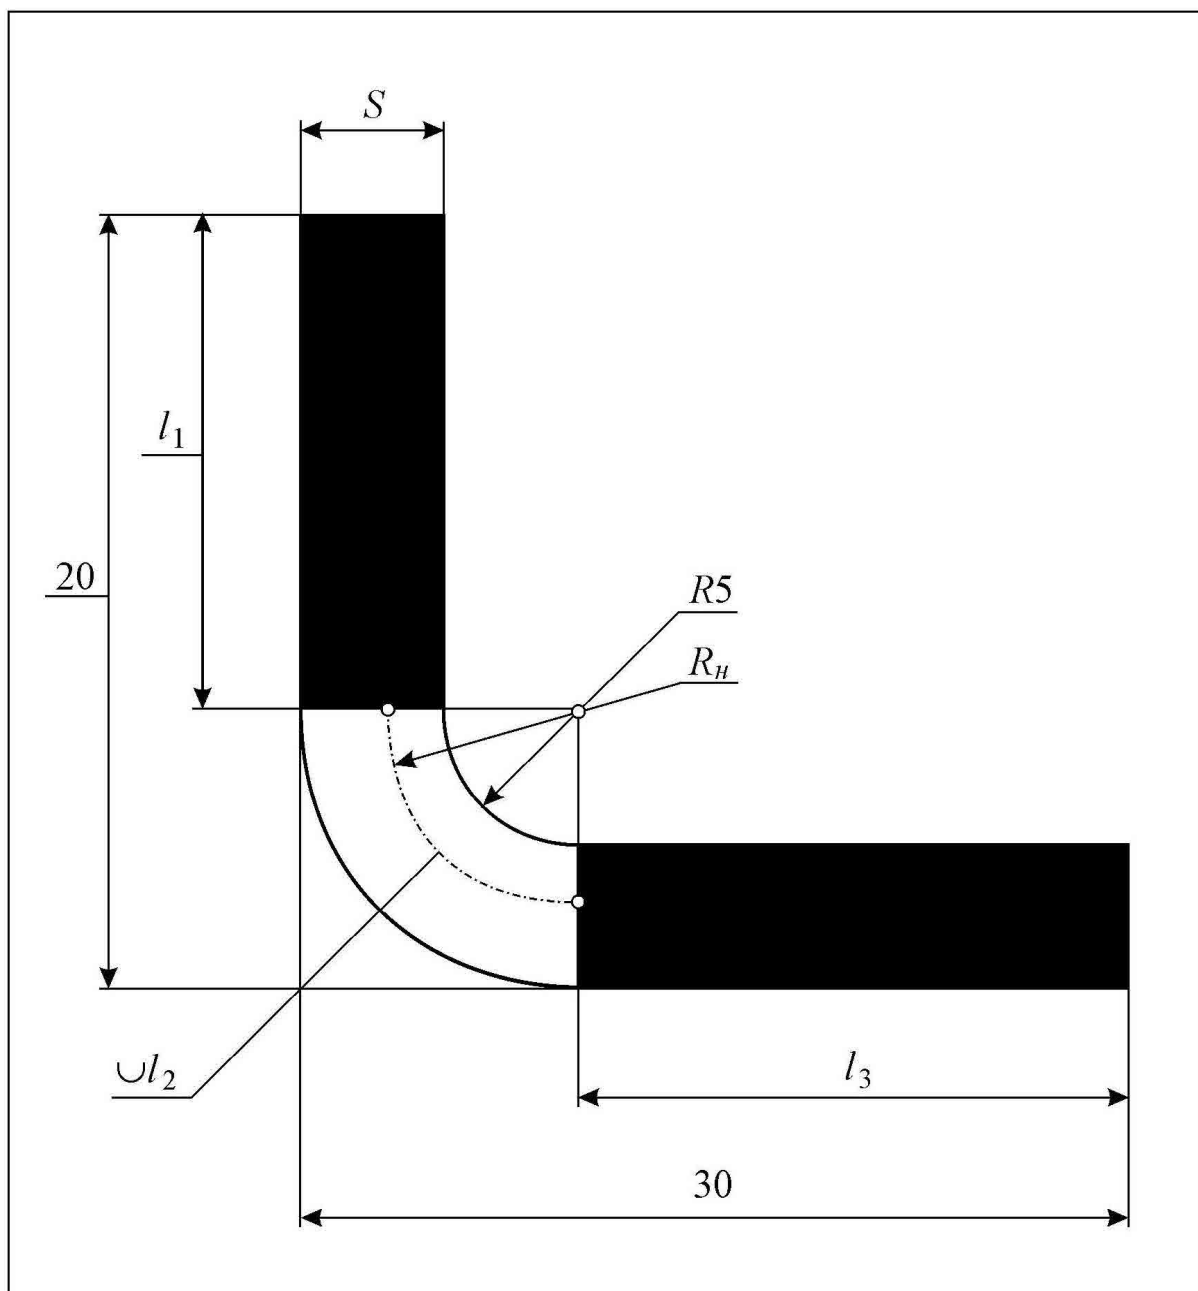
До розрахунку довжини вихідної заготовки
